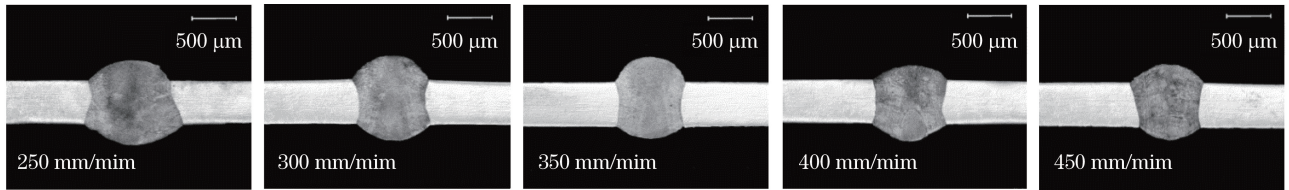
不同焊接速度下的焊缝宏观形貌
